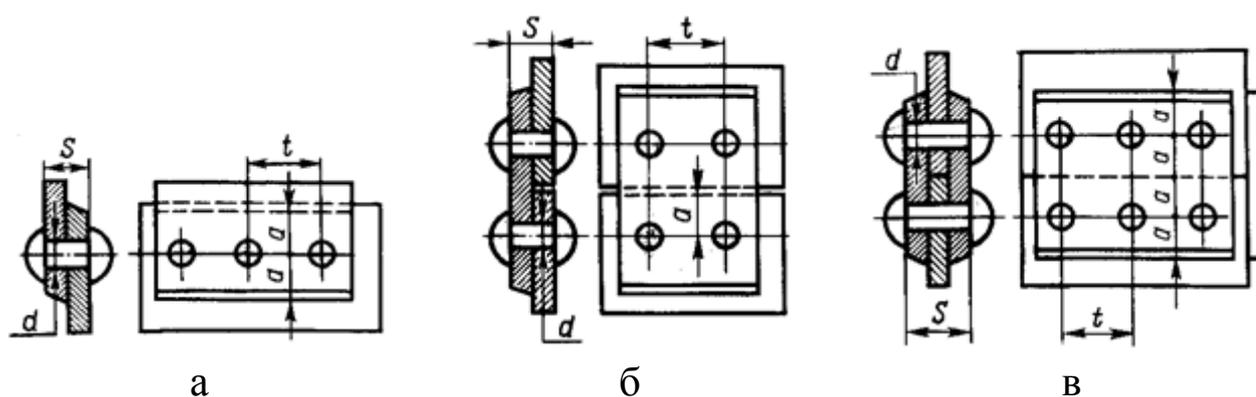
Методы клепки: а - нахлесточный; б - стыковочный с накладкой с одной стороны; в - стыковочный с двумя накладками
